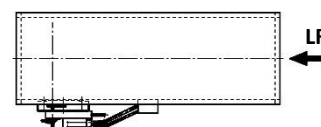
Abluft, Ausführung Links, Draufsicht
